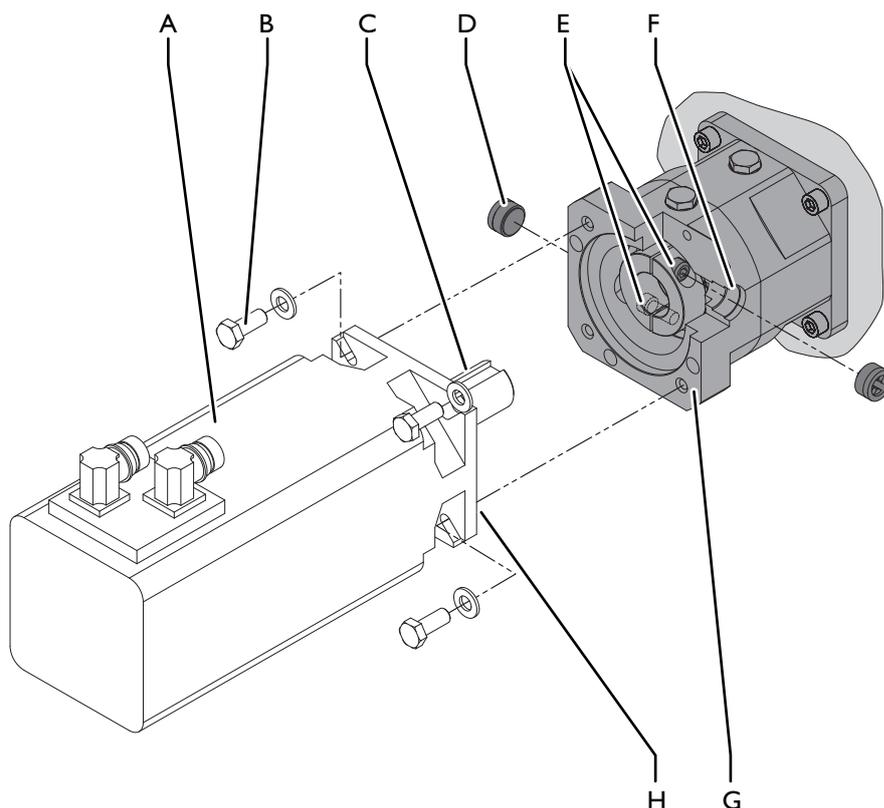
Смонтировать мотор: Планетарный редуктор Güdel
